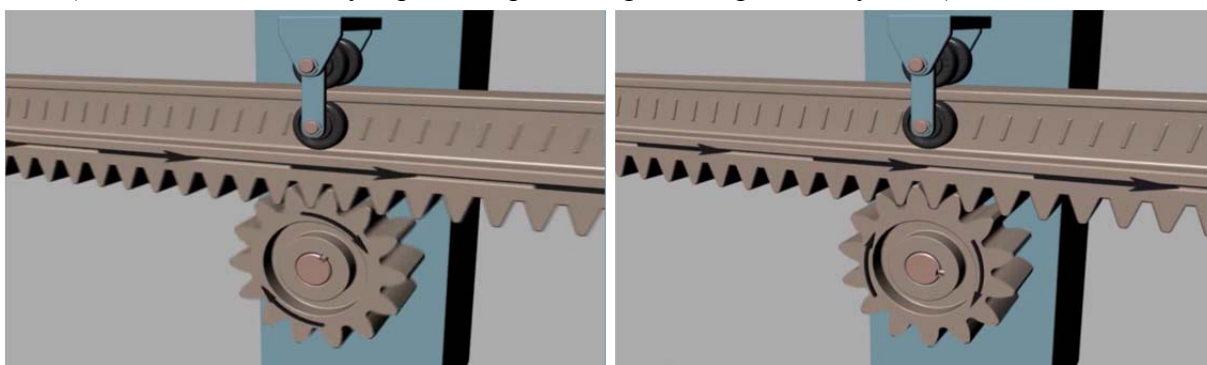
3D-модель рейкової передачі (рейка рухома)
